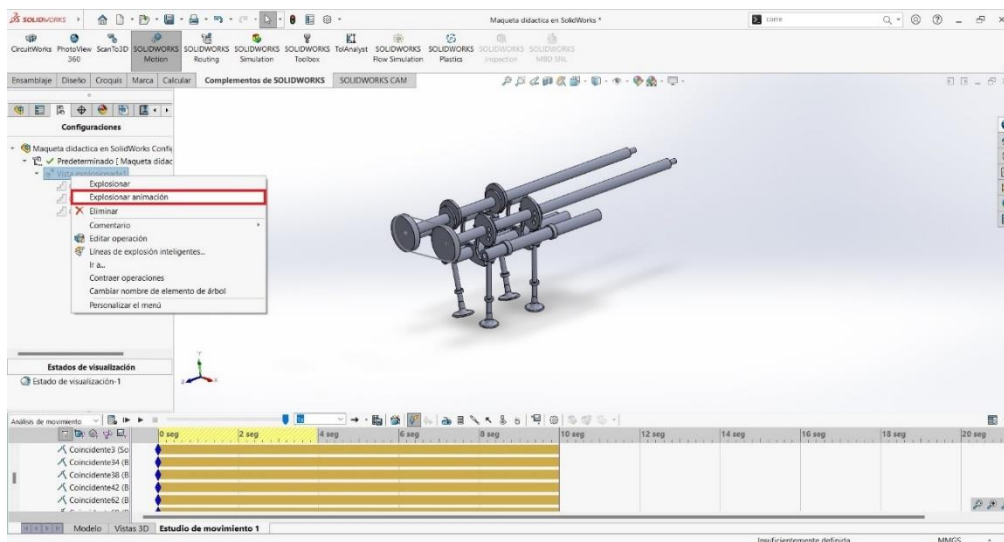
Explosionar animación. Fuente: SolidWorks
